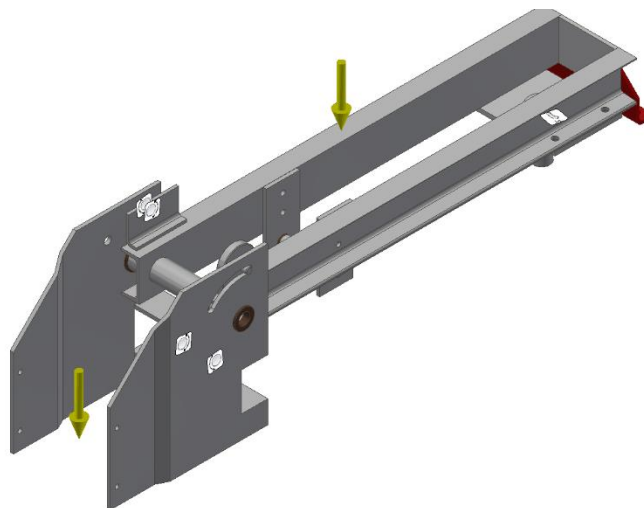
Forças e restrições aplicadas no braço lateral da estrutura
